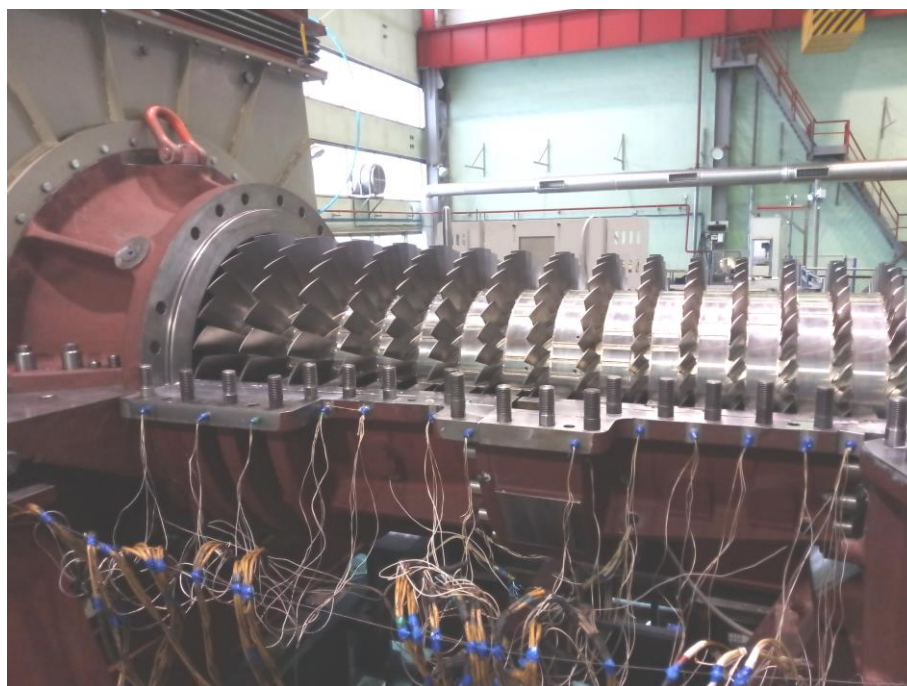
Ротор и статор компрессора ОК-2100, подготовленные к испытаниям
